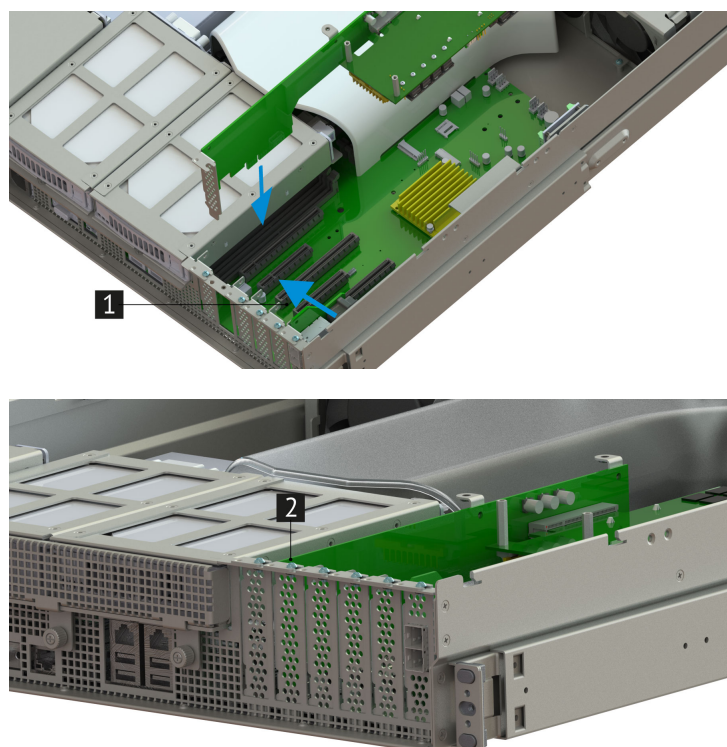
Установка адаптера поворотного НИКА.469535.023
